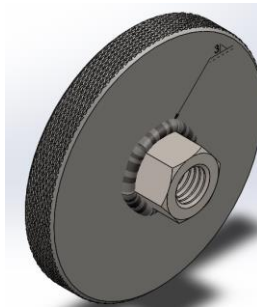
Vista 3D del ensamblaje perilla y tuerca M12.
